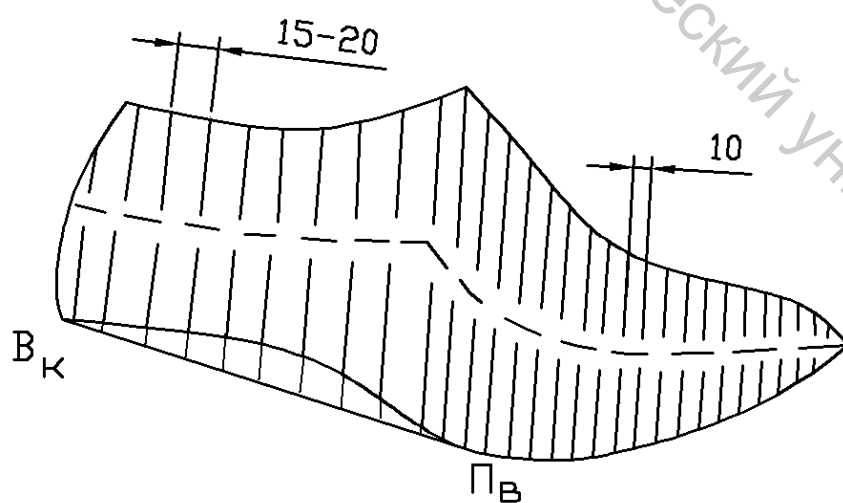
Шаблон для получения условной развертки внутренней боковой поверхности колодки
